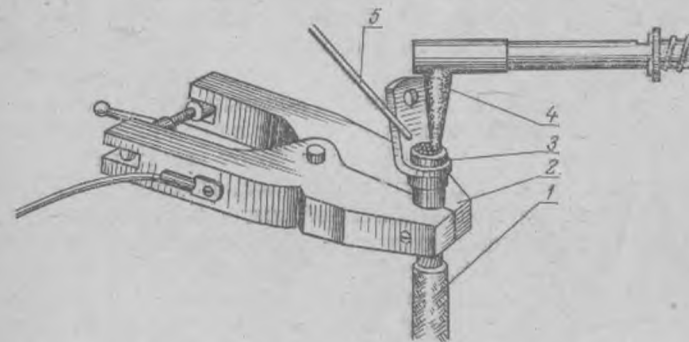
Контактная сварка алюминиевой жилы и наконечника ЛА
